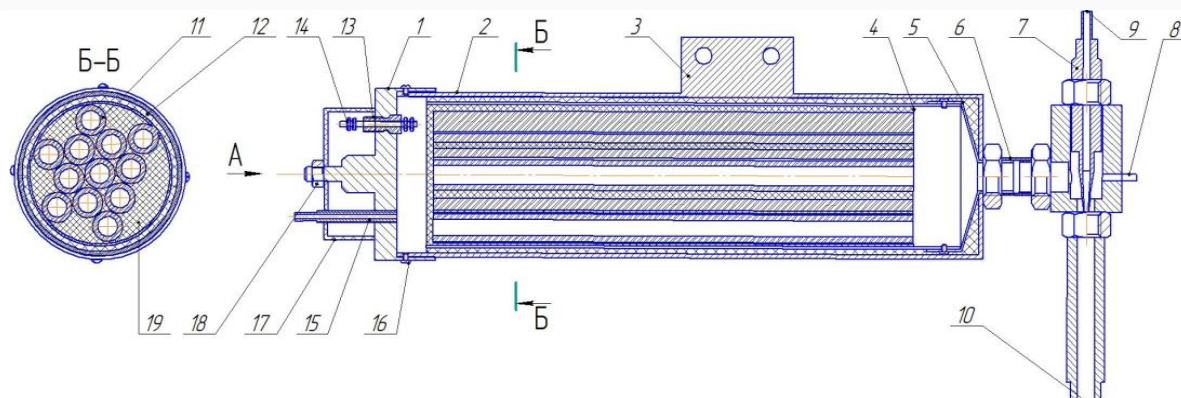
Загальний вигляд газодинамічного напилюючого пристрою
